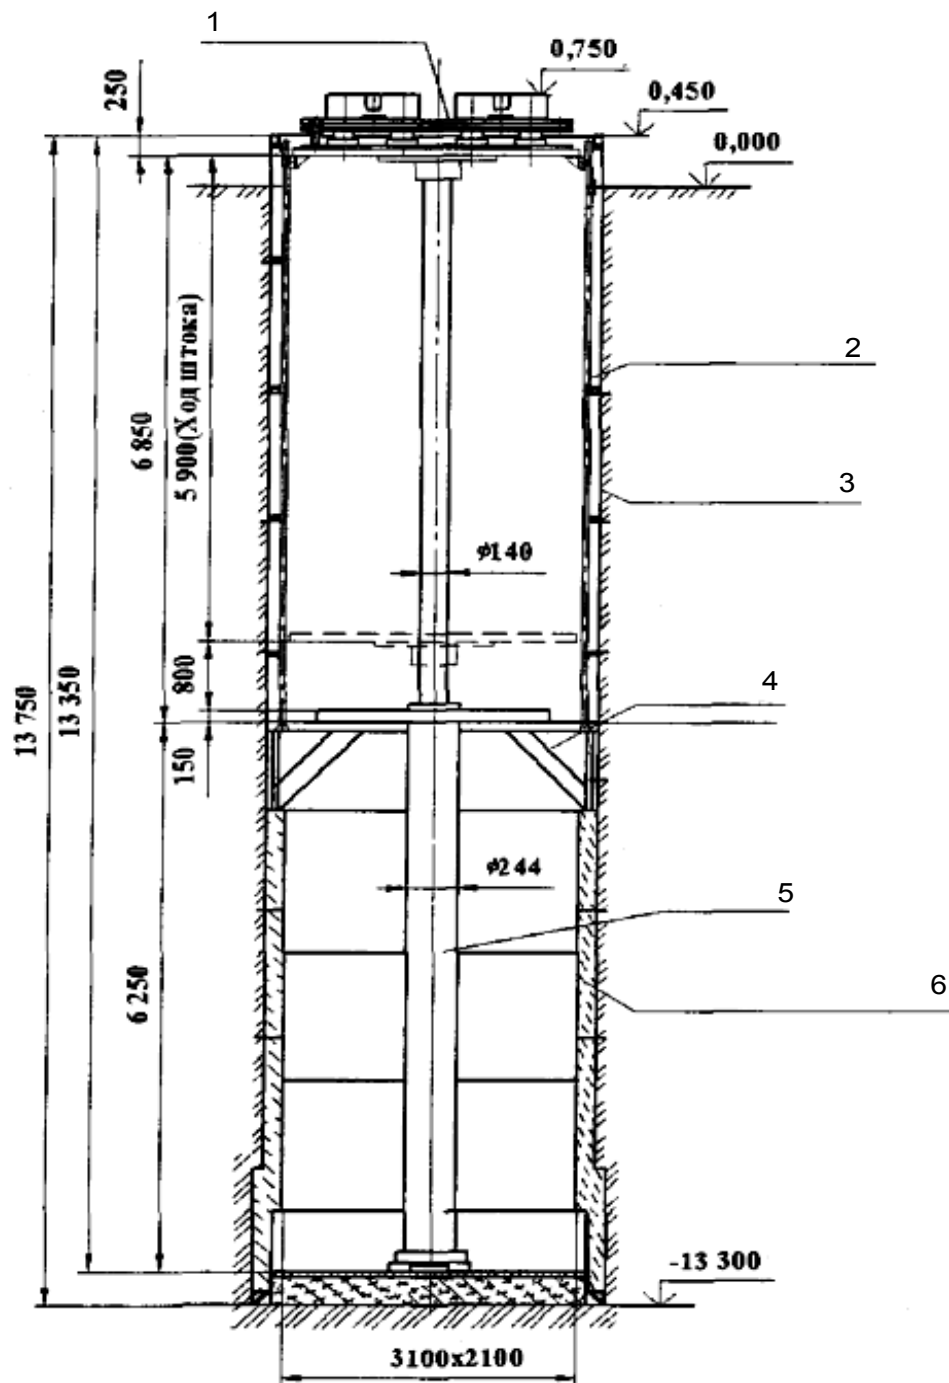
Схема машини напівбезперервного вертикального лиття алюмінієвих злитків: 1 - стіл розливки; 2 - направляючі колони; 3 - металева обичайка шахти; 4 - рама опорна; 5 - гідроциліндр; 6 - бетонна обичайка шахти
